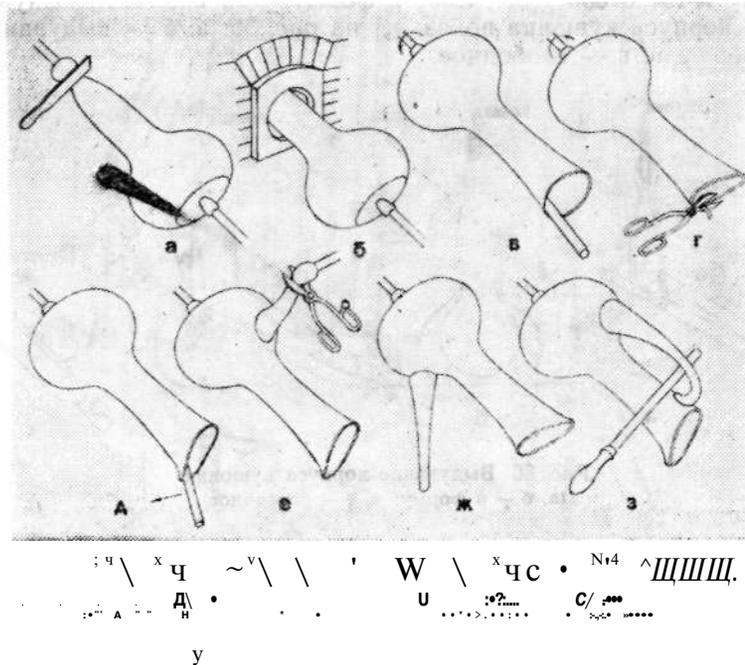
Горячая отделка горла и изготовление ручки кувшина.
